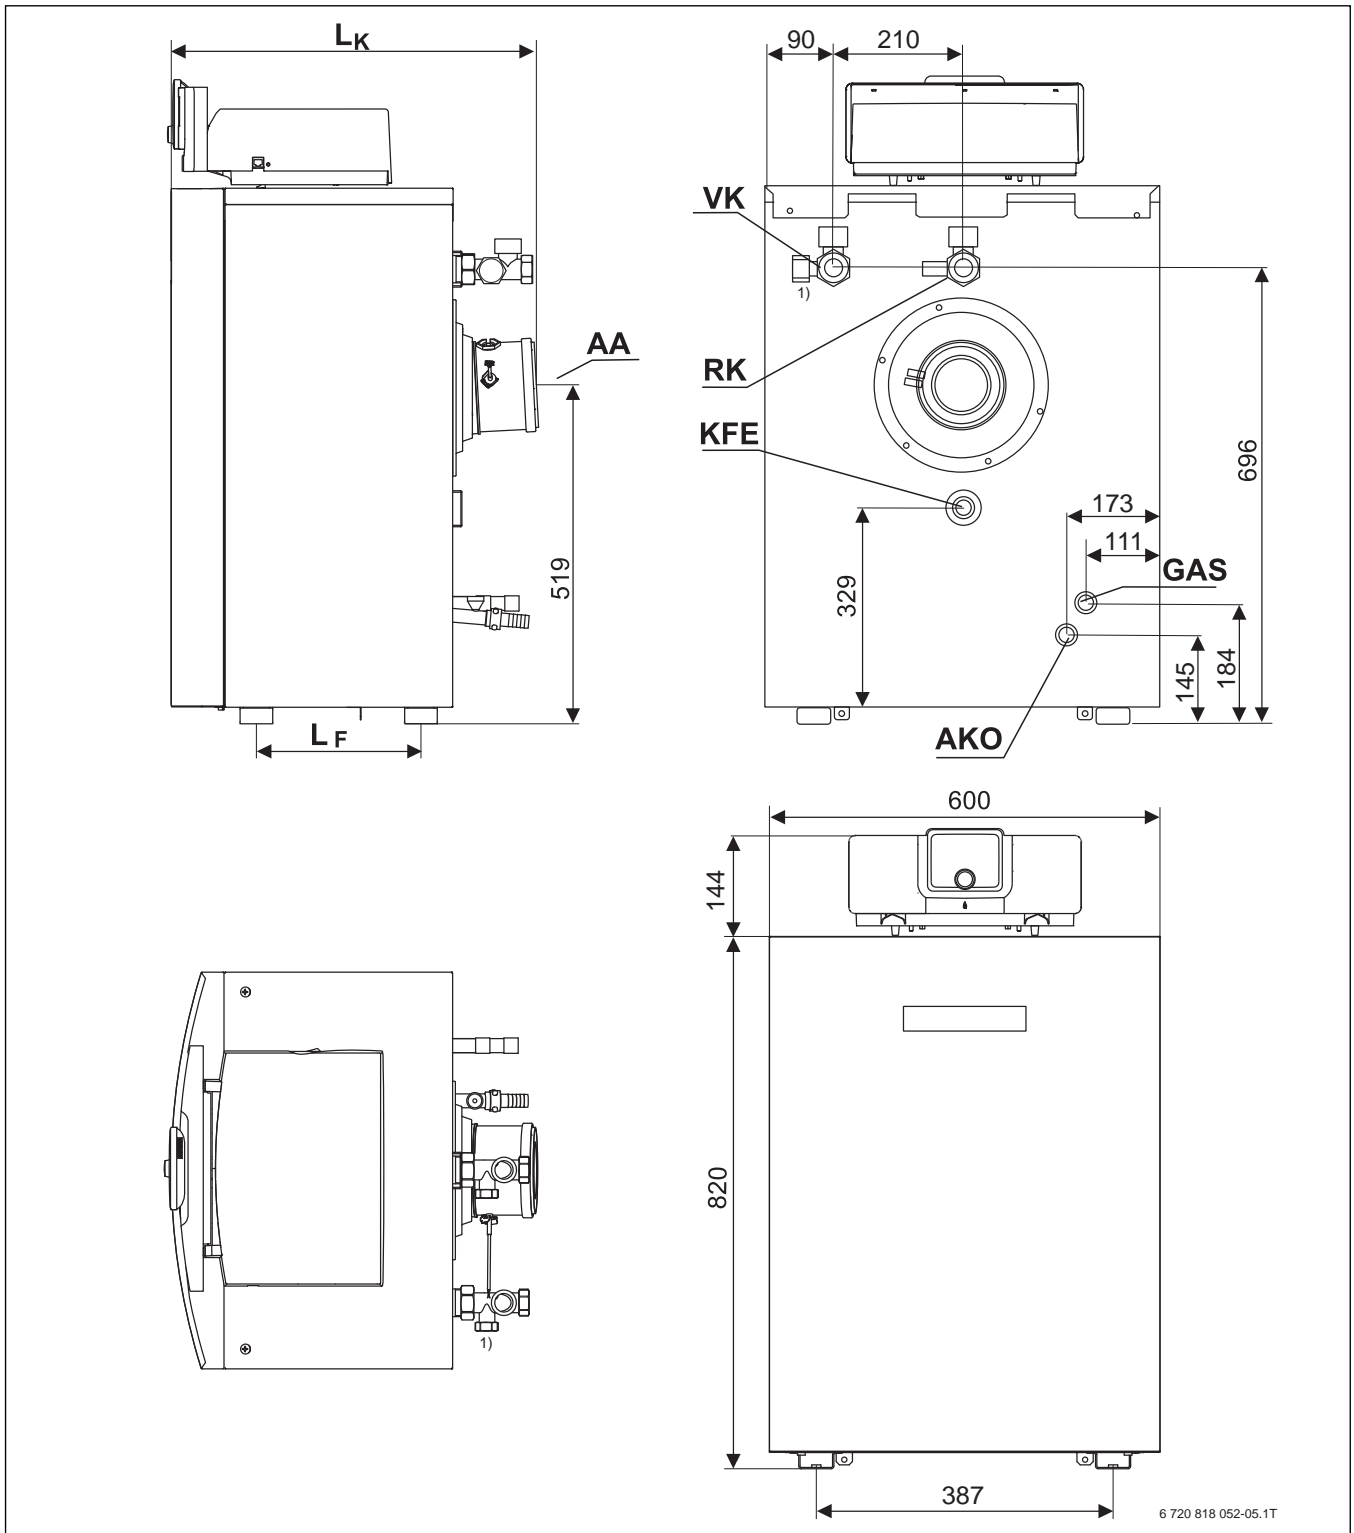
Abmessungen und Anschlüsse für Suprapur KBRC (Maße in mm)
